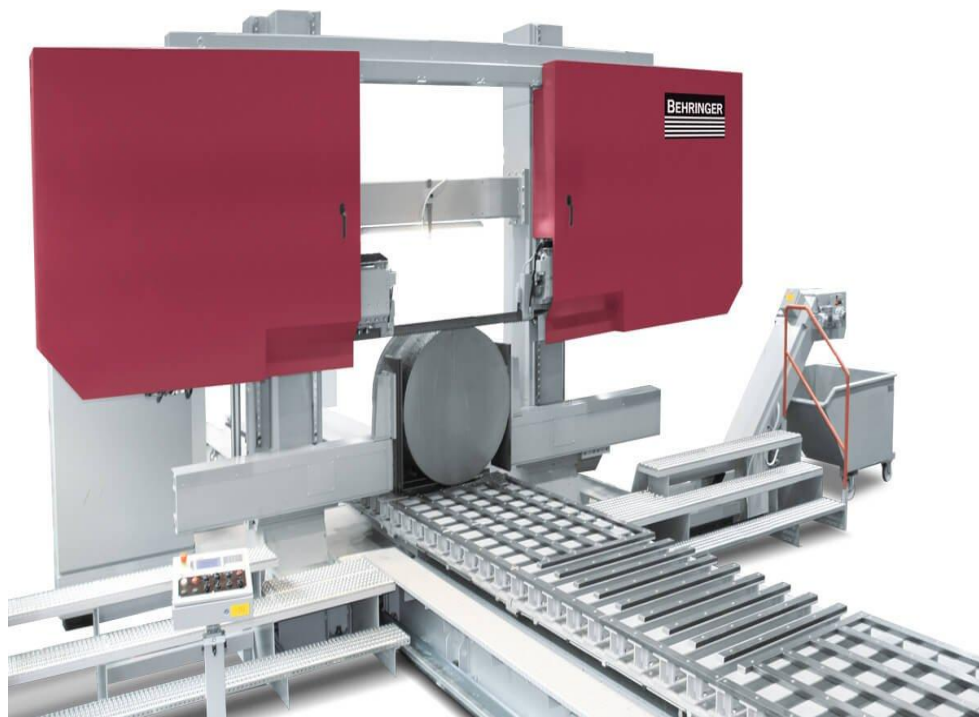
Стрічкопильний верстат BEHRINGER HBP 1100A Performance [24]
